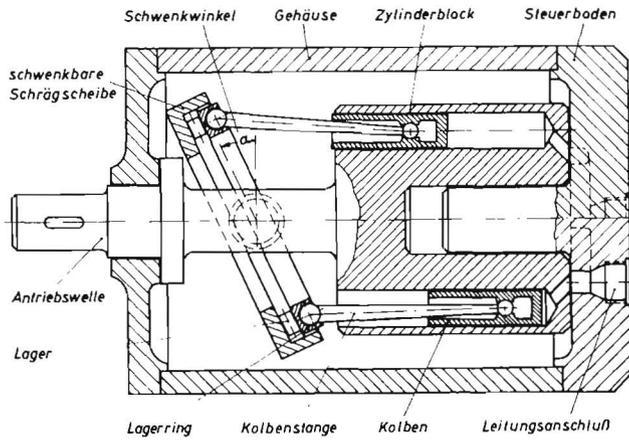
Grundaufbau der Axialkolbenmaschine mit schwenkbaren Schrägscheibe
